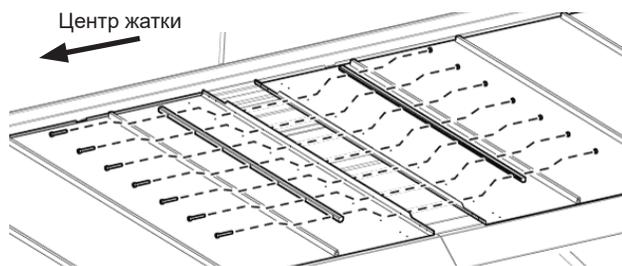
Установка соединительного стержня полотненного транспортера.
